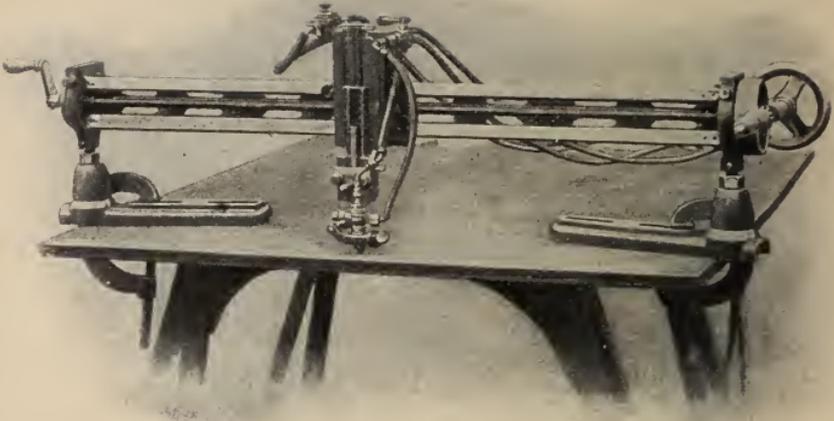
Schneidbrenner mit maschineller Führung für 1 m Schnitlänge.
